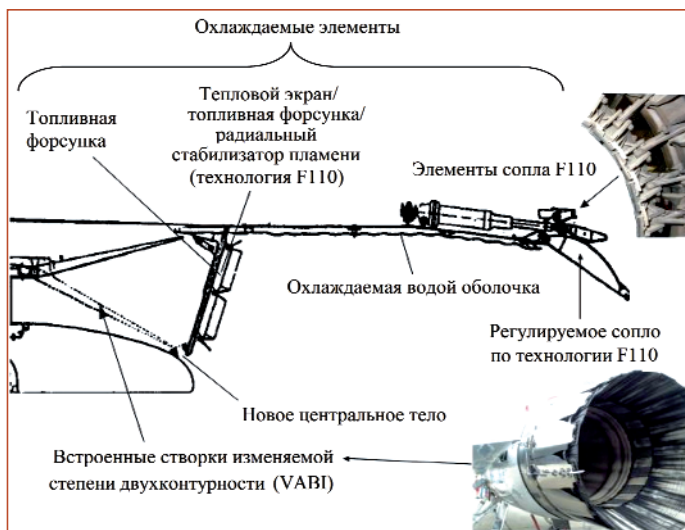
Конструктивная схема форсажной камеры и сопла RTA-1
